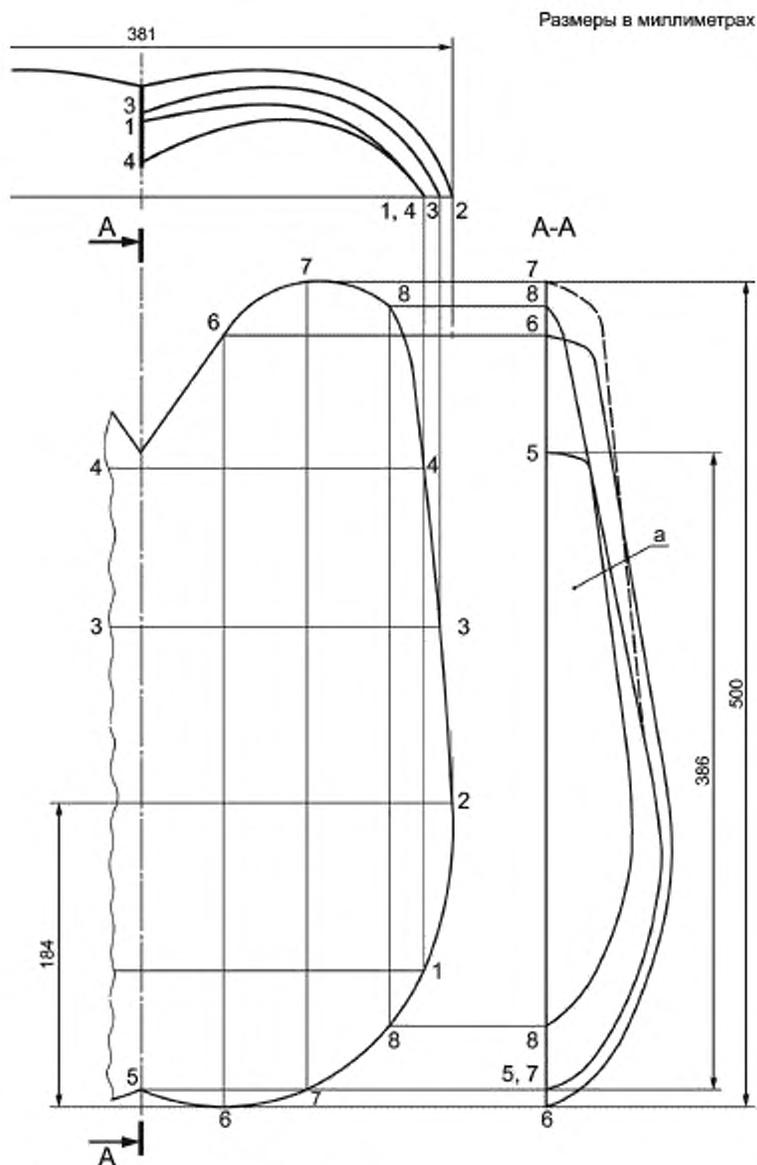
Линейные размеры подушки нагружения — Конструкция из древесины твердых пород
